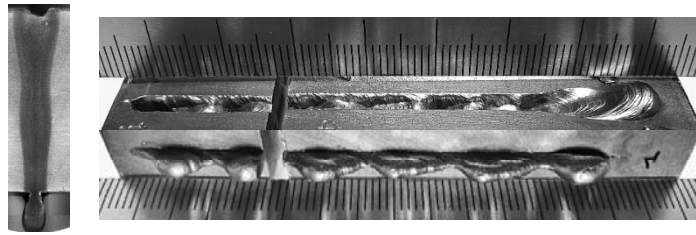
Внешний вид поверхности и корня сварного шва без развертки электронного луча
